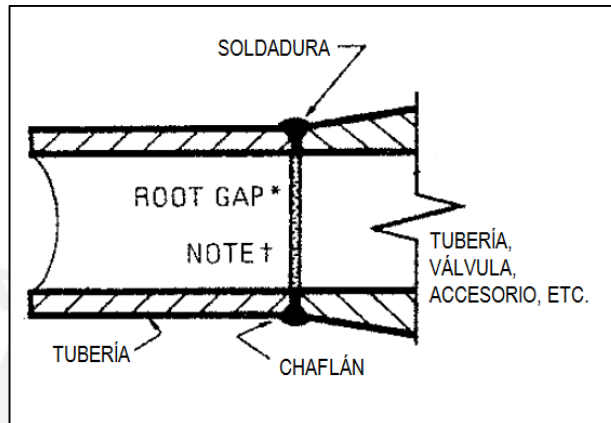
Soldadura a tope. (Adaptado de Sherwood, 1991)
